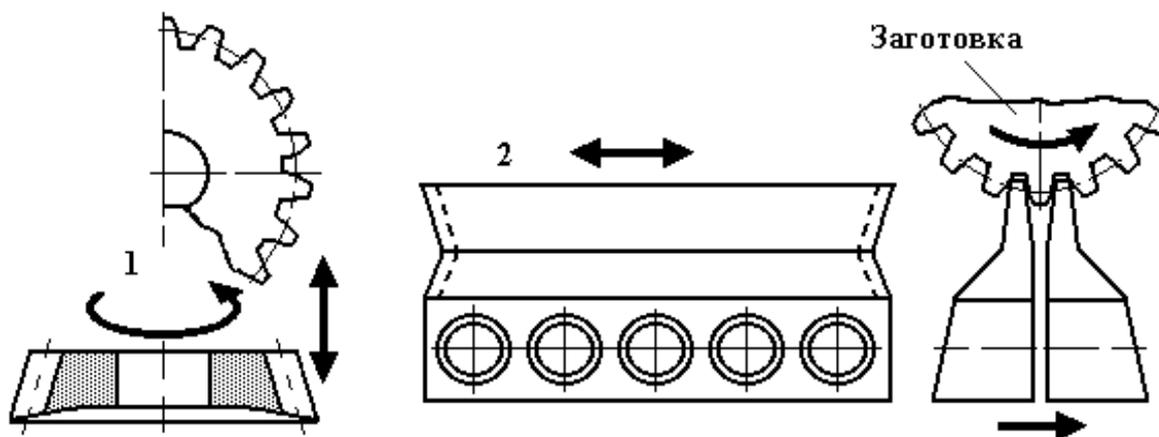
Инструмент для зубонарезания по методу обкатки: 1 – зуборезный долбяк; 2 – зубострогальный резец
